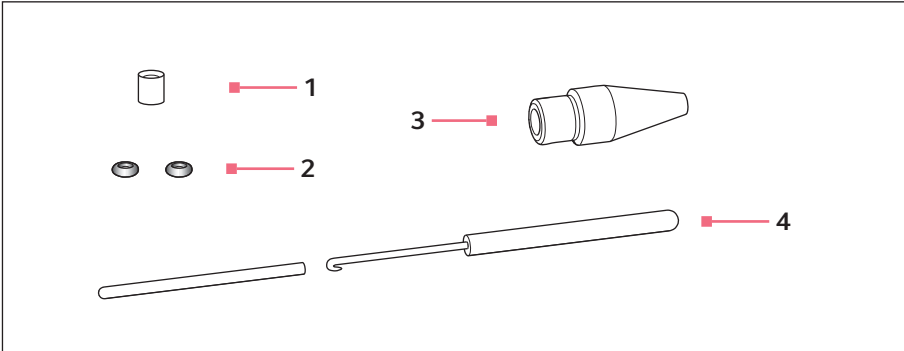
Spannkopf 4 mit Entnahmewerkzeug
